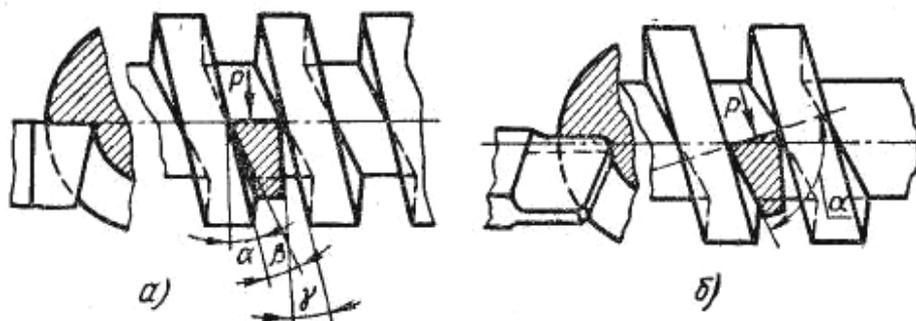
Схемы установки резцов при нарезании резьбы
